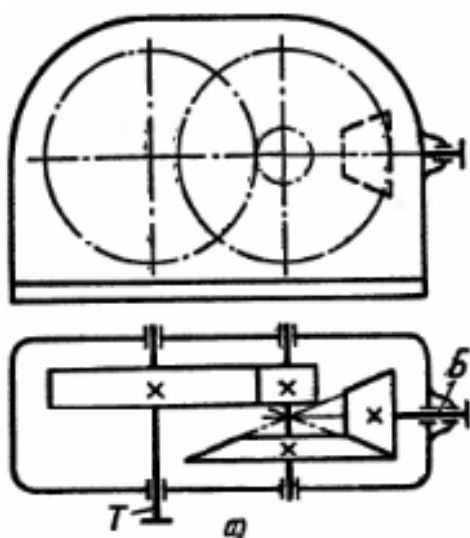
Коническо-цилиндрический двухступенчатый горизонтальный редуктор:
